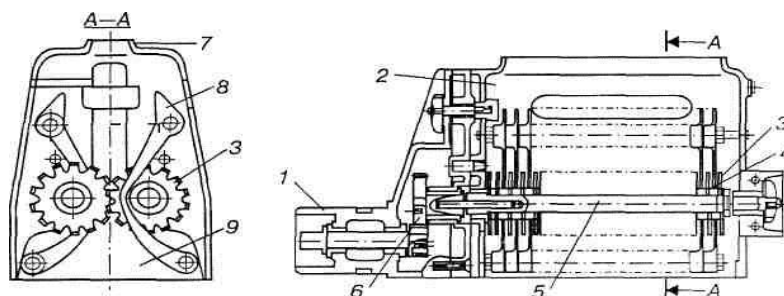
Механізм МРП - II - I для розпушування м'яса:
